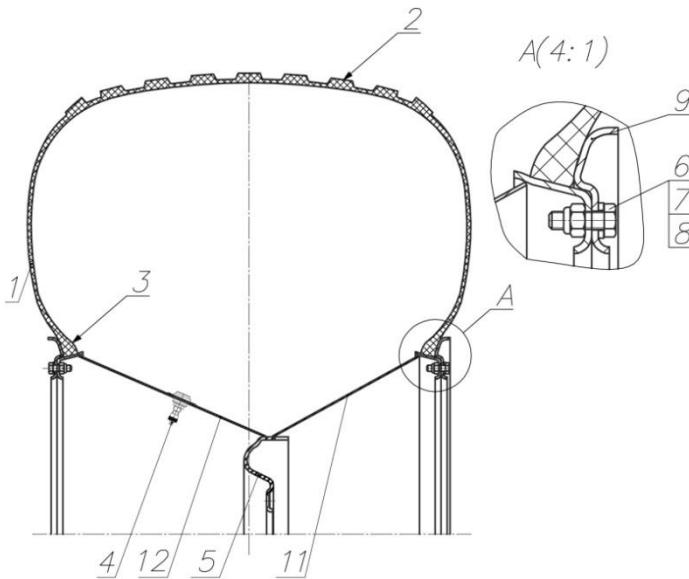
Шина 1300x600-533 ТРЭКОЛ с колесом в сборе
